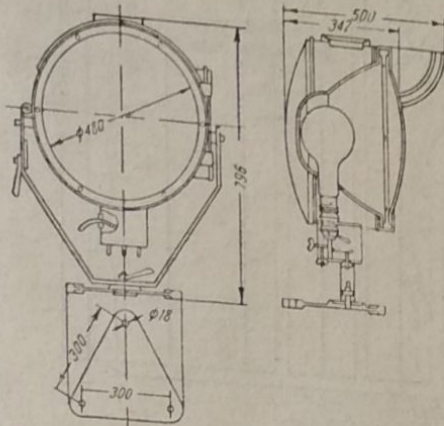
Общий вид с установочными размерами прожектора типа ПЗ-45
